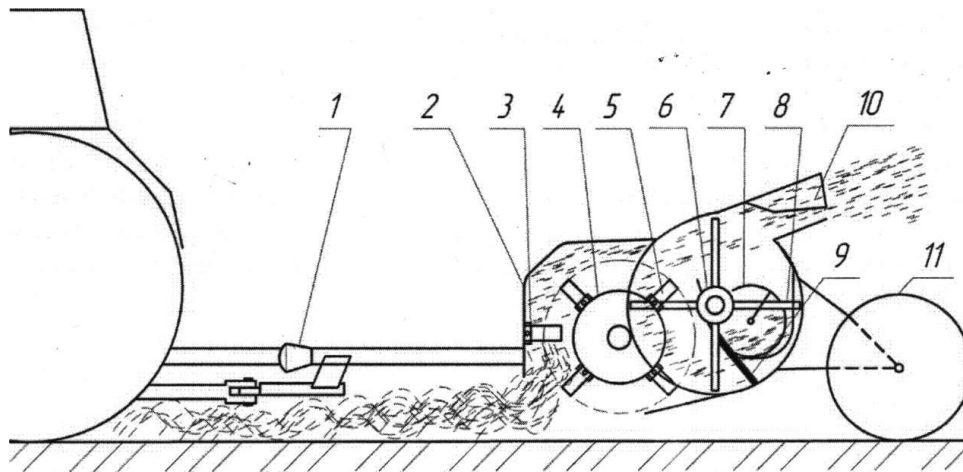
Технологическая схема 2 прицепного измельчителя-разбрасывателя соломы с двухстадийным измельчением: 1 - карданный вал; 2 - корпус измельчителя; 3 - противорезы; 4 - роторный подбирающий аппарат (измельчающий барабан); 5 - нож измельчающего барабана; 6 - барабан доизмельчитель; 7 - шнек; 8 - нож; 9 - противорезущая пластина; 10 - распылитель; 11 – колесо
